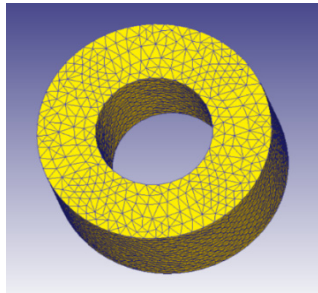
Розбивка вхідної заготовки для формування фланця на скінчені елементи
